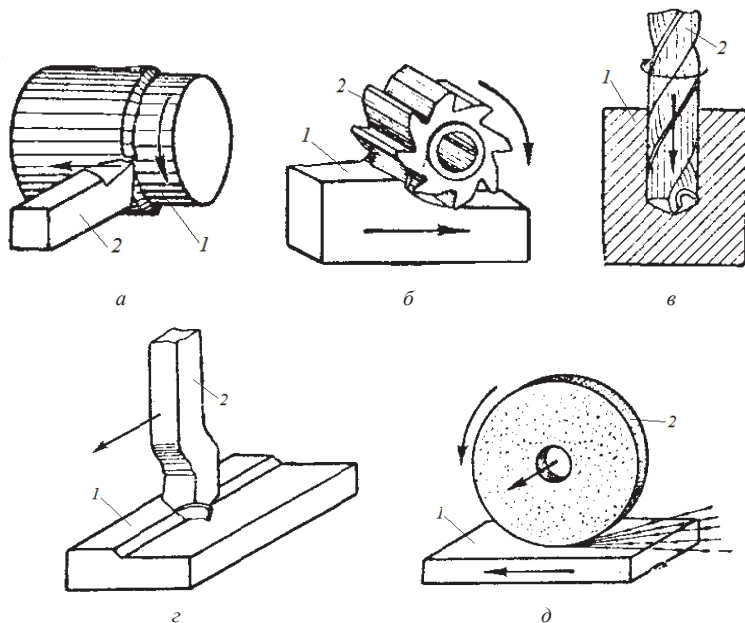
Схемы основных технологий обработки металлов резанием: *a* – точение; *b* – фрезерование; *в* – сверление; *г* – строгание; *д* – шлифование; 1 – заготовка; 2 – инструмент
